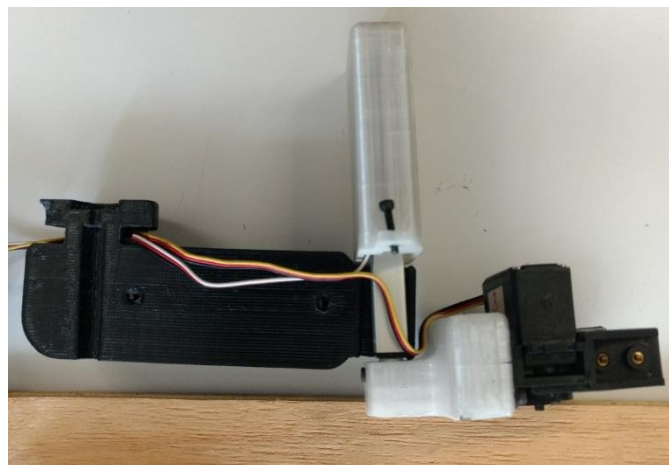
Parte del ensamble gripper, actuador lineal y el vínculo dos
